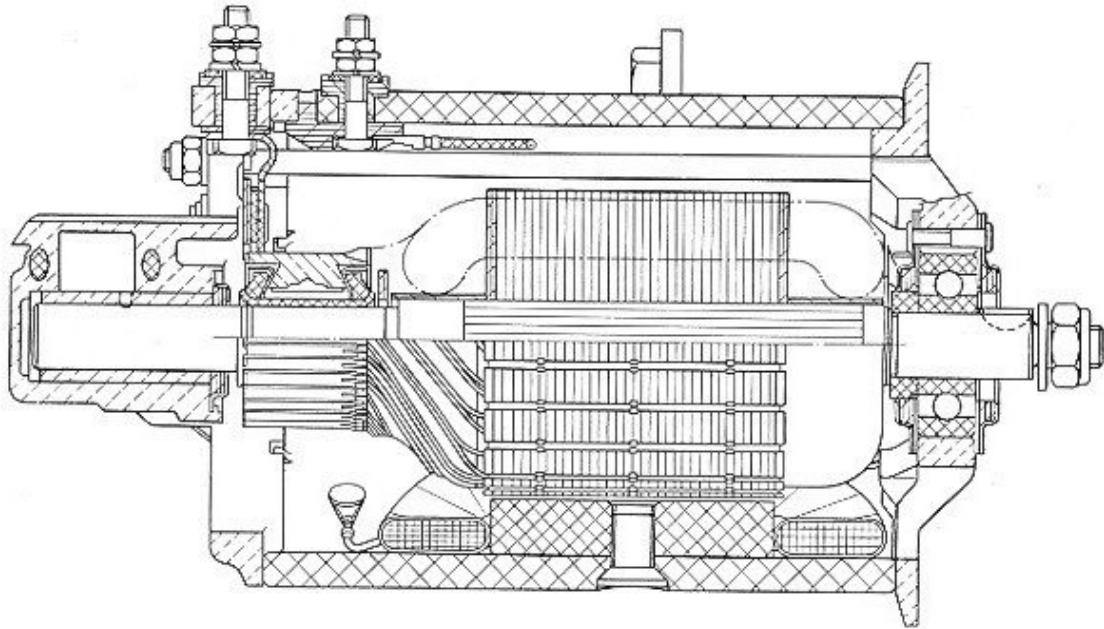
Längsschnitt durch die Lichtmaschine.
